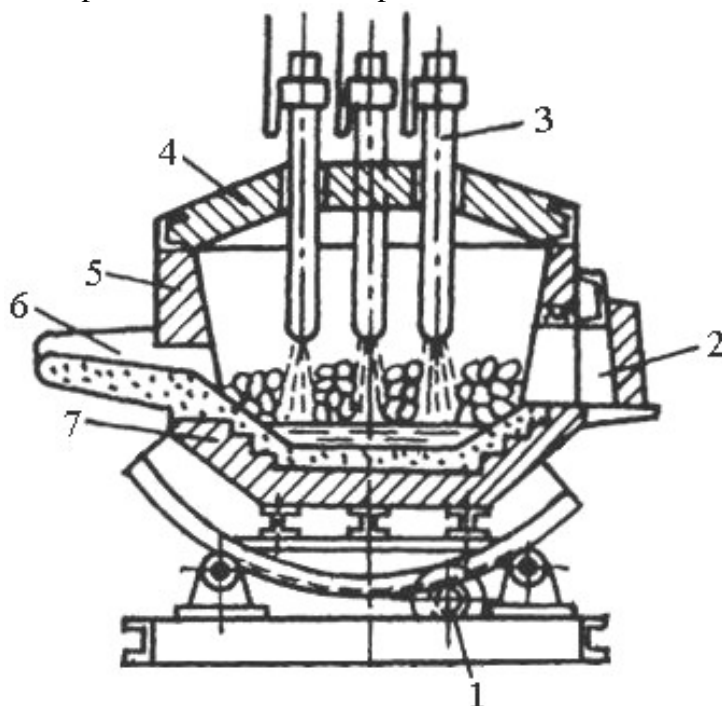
Схема трехфазной дуговой печи: 1 – механизм поворота печи; 2 – загрузочное окно; 3 – электроды; 4 – свод; 5 – корпус; 6 – желоб для выпуска стали; 7 – под печи
